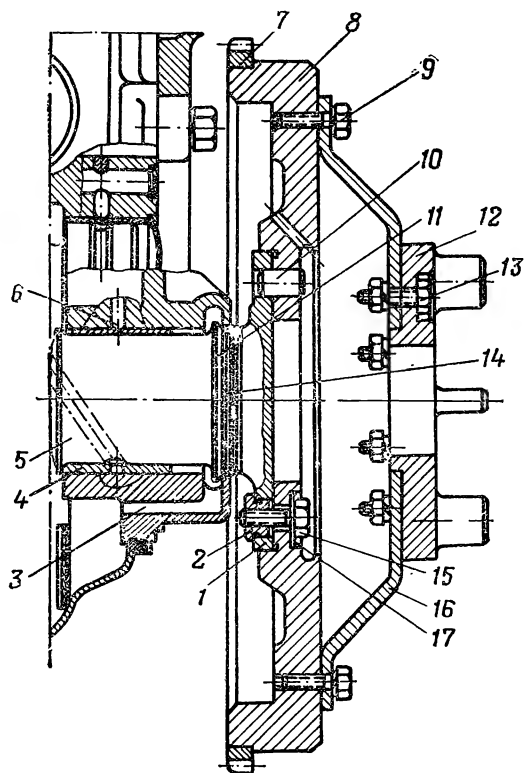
Задняя коренная шейка, уплотнение заднего конца коленчатого вала, крепление маховика и полумуфты:
